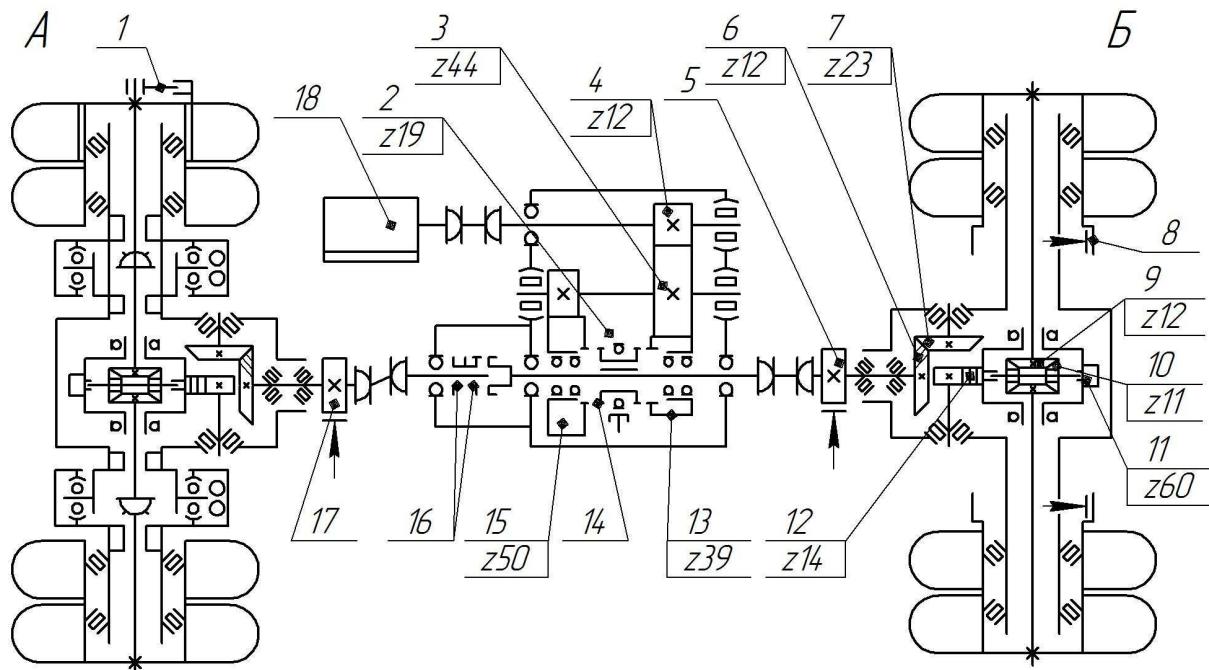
Кинематическая схема механизма передвижения крана КС-5363: 1 – поводок, 2-4, 6, 7, 9, 13, 15 – шестерни, 5, 8, 17 – тормоза, 14 – кулачковая втулка, 16 – эвольвентные шлифы, 18 - электродвигатель
